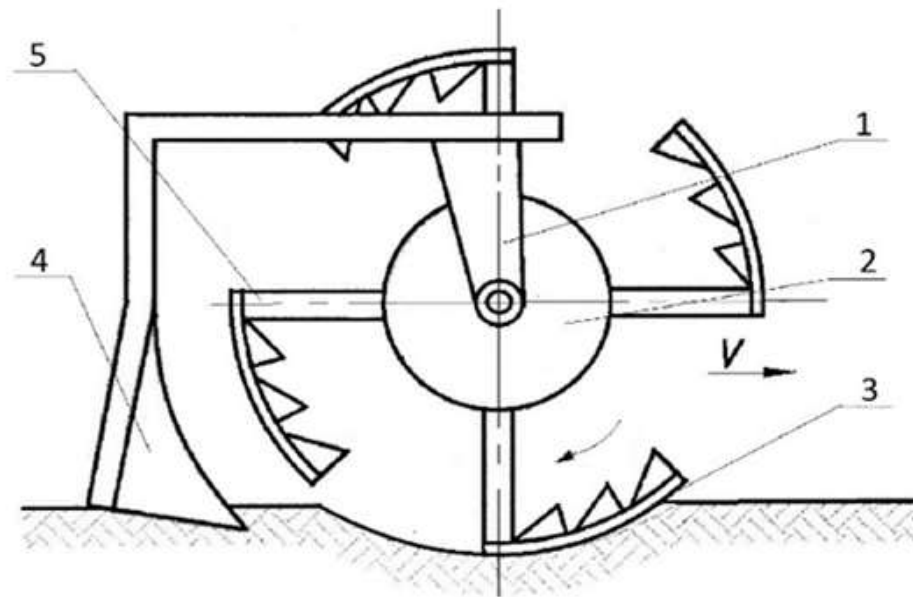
Схема пристрою для обробки ґрунту, (вигляд збоку).
